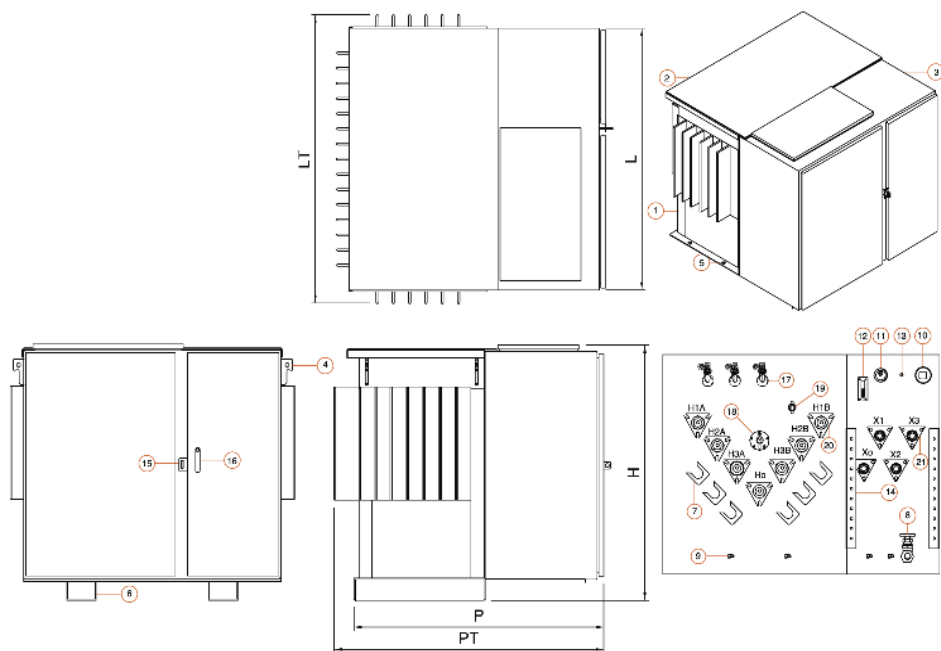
Partes de un transformador trifásico padmounted Tipo Malla
